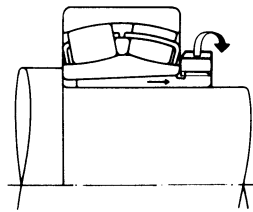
Remoção da Bucha de Desmontagem (1)
